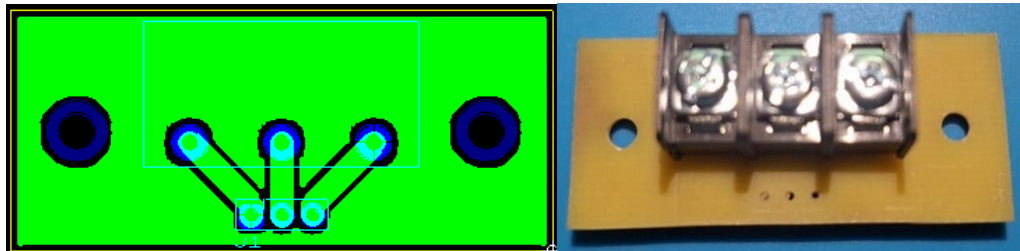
Diseño y manufacturación del PCB para la conexión del transductor PT100
